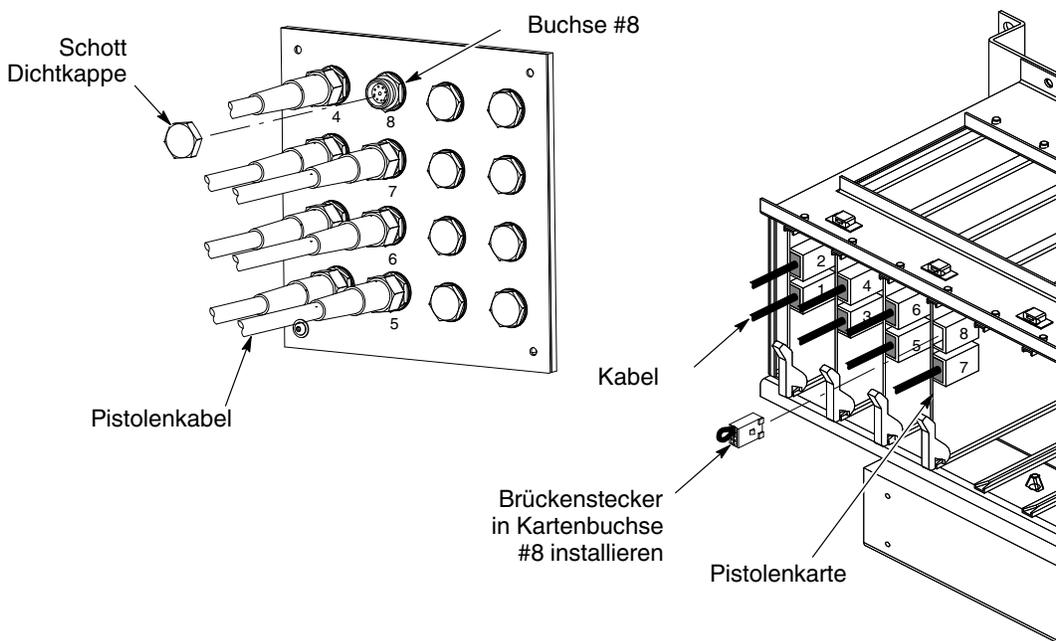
Dichtkappe und Brückenstecker installieren - Beispiel mit 7 Pistolen in einem System für 8 Pistolen
